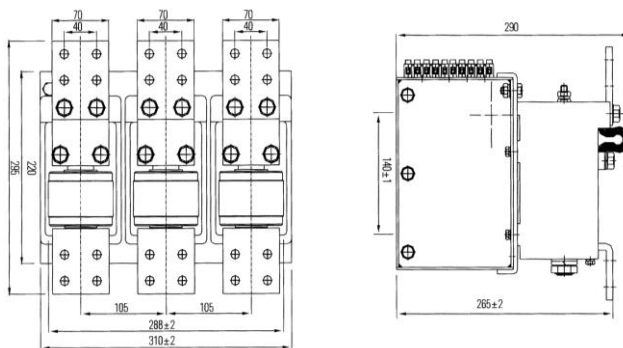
Габаритные размеры КВТ-1,14-1000/1250
